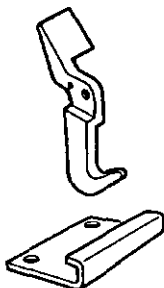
Enclavamiento de extracción aparato armado VEAA.
